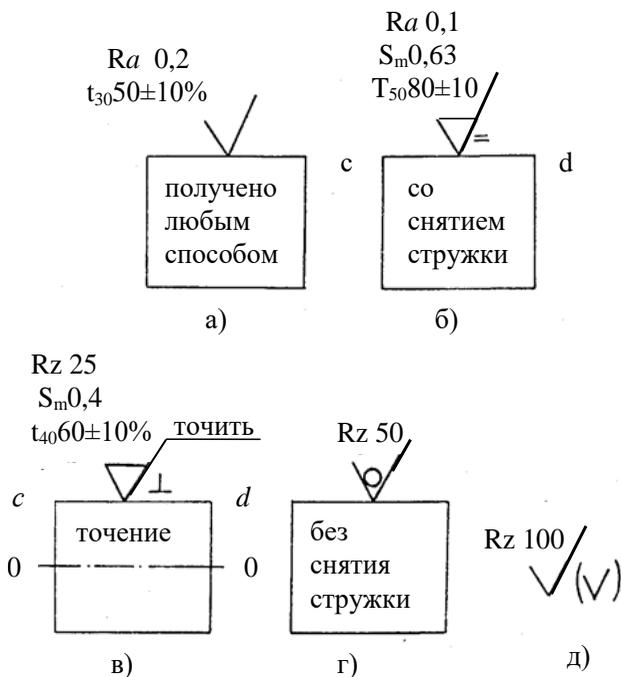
Обозначение шероховатости поверхности на чертежах
